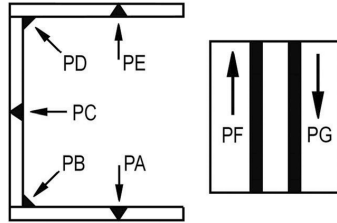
Dénominations des positions de soudage pour les soudures bout à bout.
